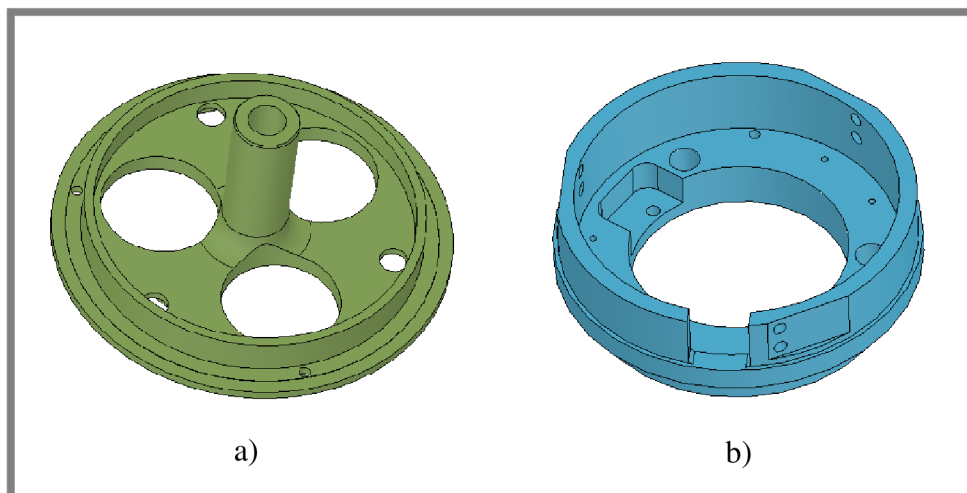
Upevnění vnějšího kroužku ložiska a) horní disk b) spodní disk
